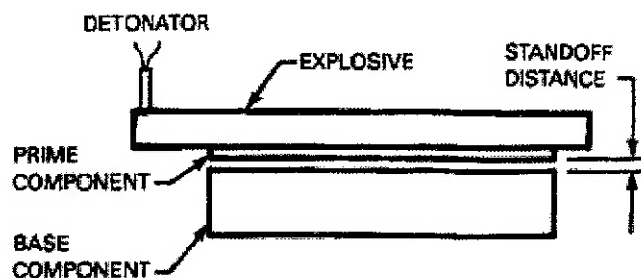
Arranjo típico dos componentes para revestimento por explosão. Adaptado da ref. [20].
